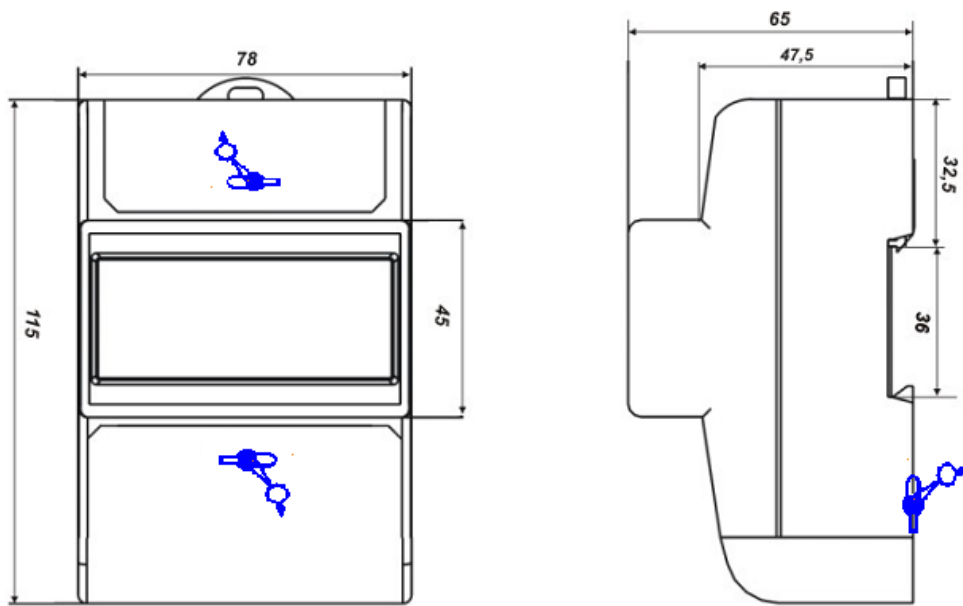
Габаритный чертеж и установочные размеры счетчика (для счетчиков с типом корпуса Н3)
